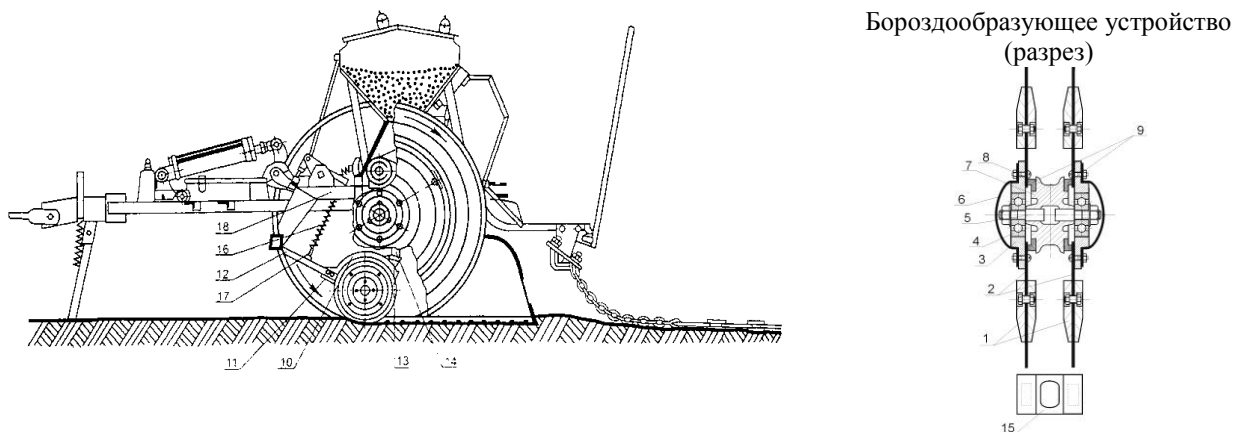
Модернизированная сеялка: 1 – дисковый нож, 2 – бороздообразующая накладка, 3 – ступица, 4 – крышка, 5 – подшипник, 6 – болт, 7 – боковой выступ, 8 – корпус, 9 – резиновый уплотнитель, 10 – гребень, 11 – гнездо, 12 – поводок, 13 – раструб, 14 – семяпровод, 15 – делительная воронка, 16 – пружина, 17 – штанга, 18 – вилка подъема, 15 – делительная воронка
